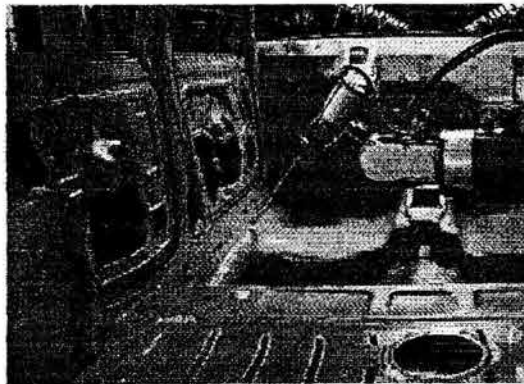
En las cadenas de montaje, se ha robotizado el proceso de protección de los rincones más sensibles de las carrocerías
